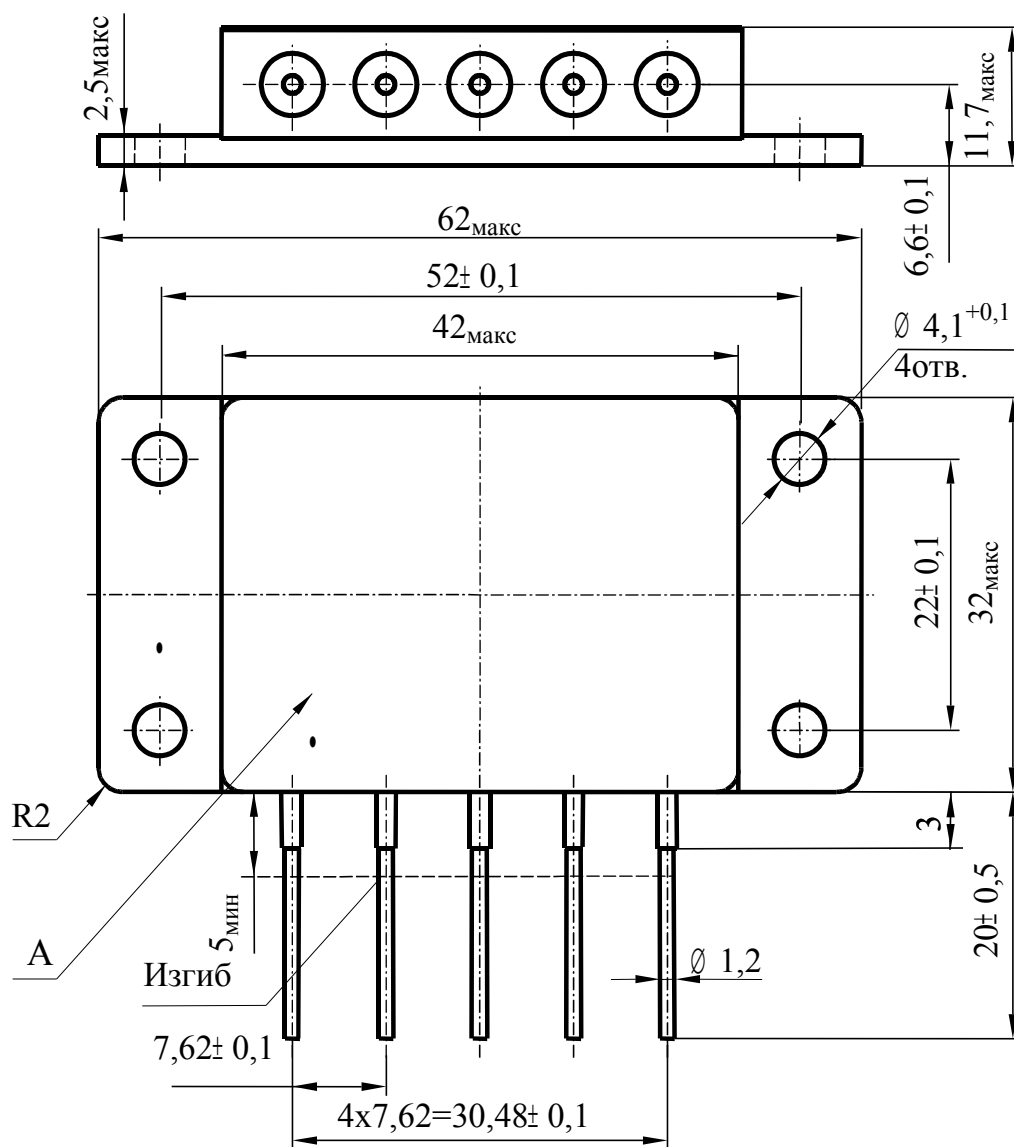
Габаритный чертеж ЯВД.432325.015ГЧ
